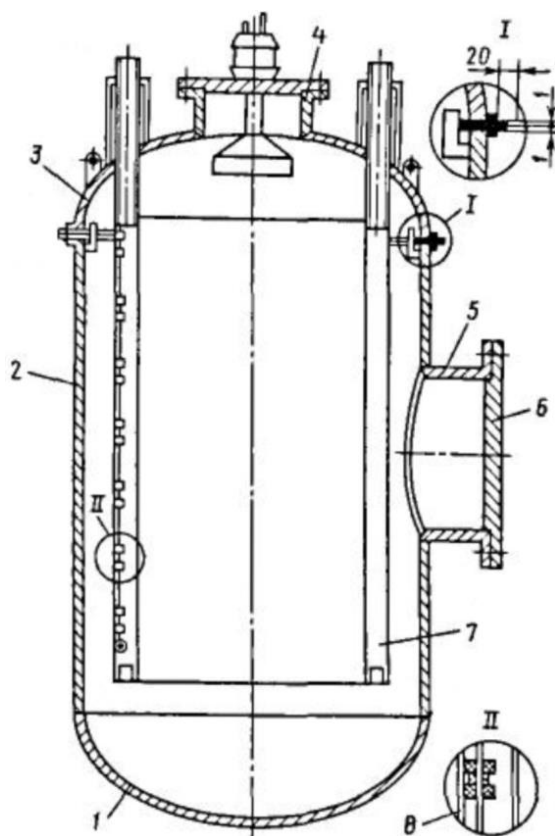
Высоковакуумная камера: 1-днище, 2-цилиндрическая обечайка, 3- днище-крышка, 4,5-патрубки, 6-фланец, 7-внутренний полый сосуд, 8- нагреватель
